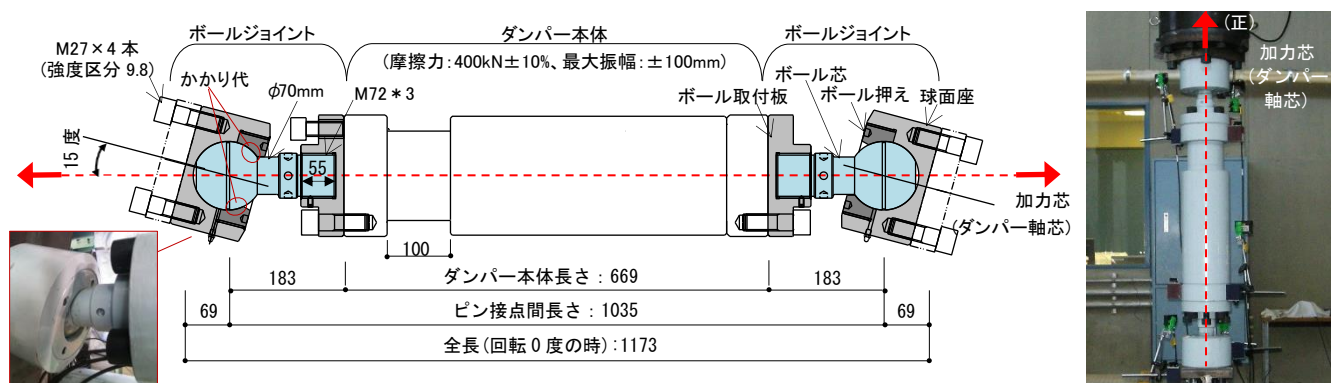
400kN級 橋梁用摩擦ダンパーの外観(ボールジョイント15度回転時の断面図) 写真-1 ボールジョイント付き摩擦ダンパーの試験状況
